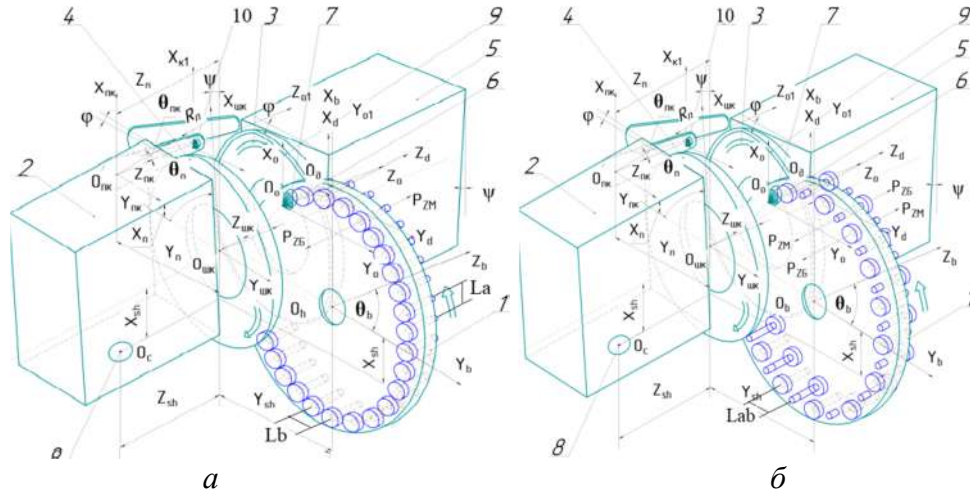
Розрахункова схема формоутворення торців деталей різних діаметрів з двома способами розташування їх у барабані подачі
